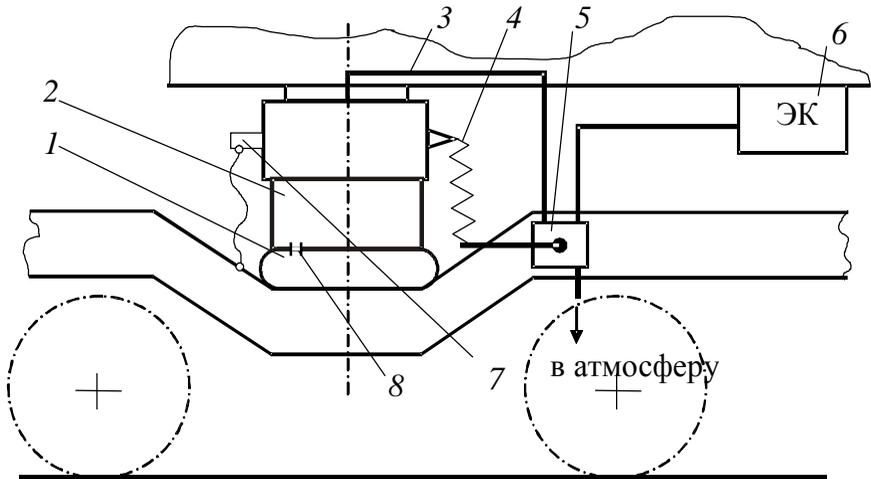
Схема пневматического рессорного подвешивания задней тележки
